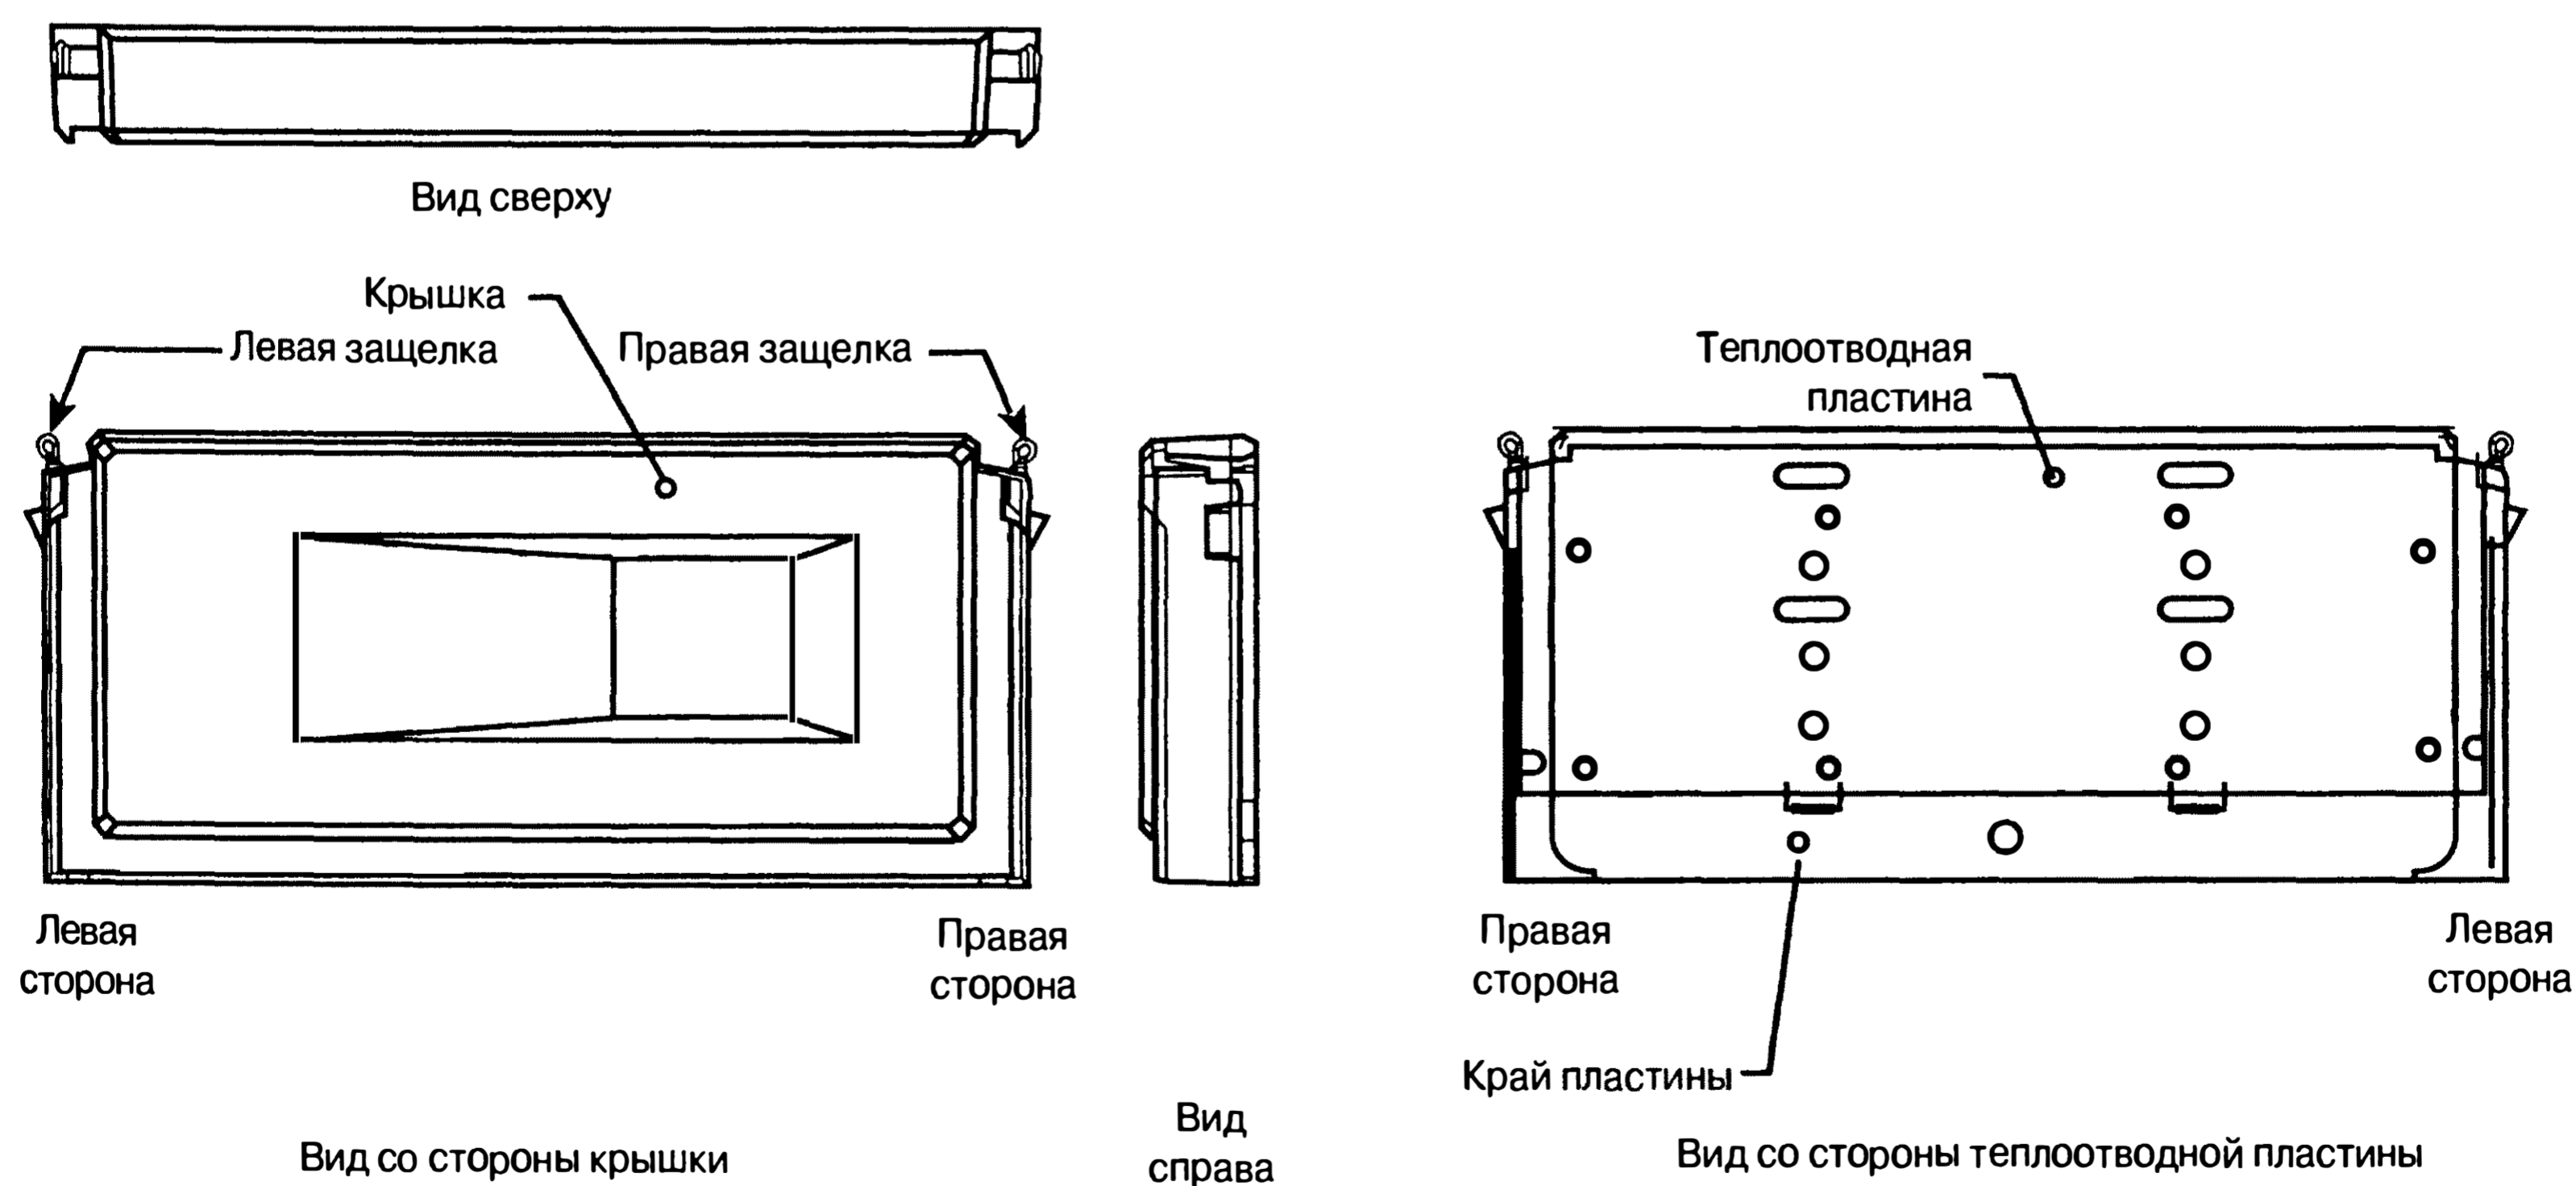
Детали корпуса SEC для процессора Pentium II
